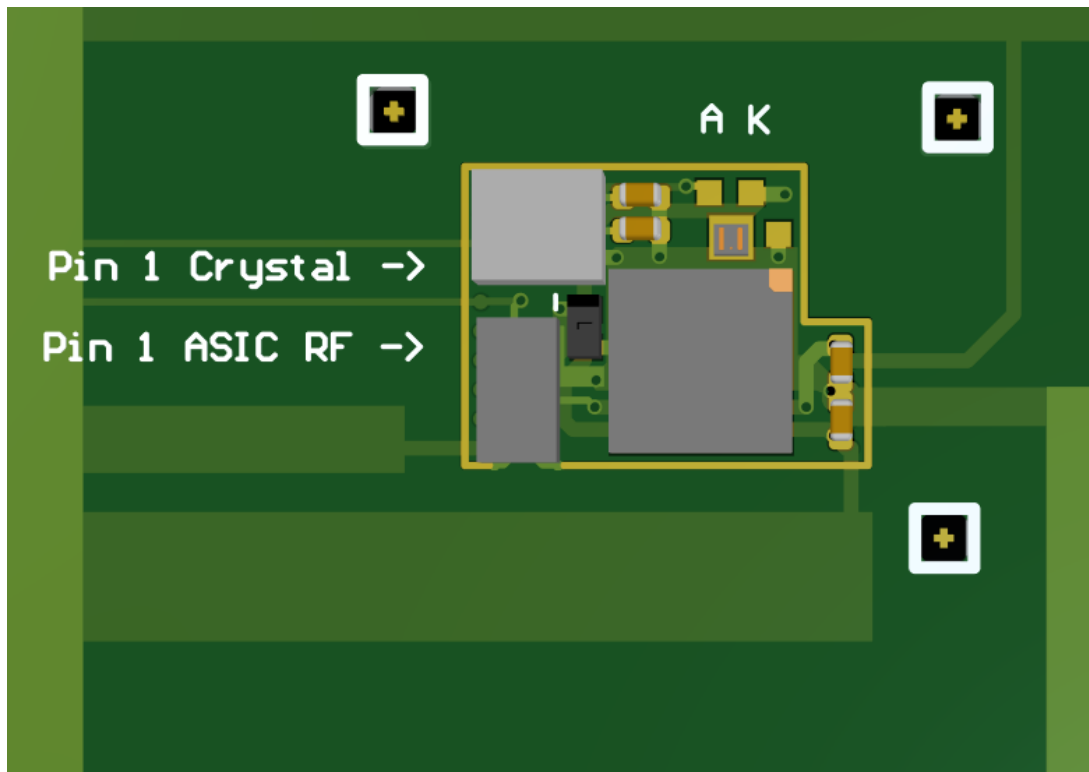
Image agrandie sur les composants de la face de dessus du PCB interposeur
